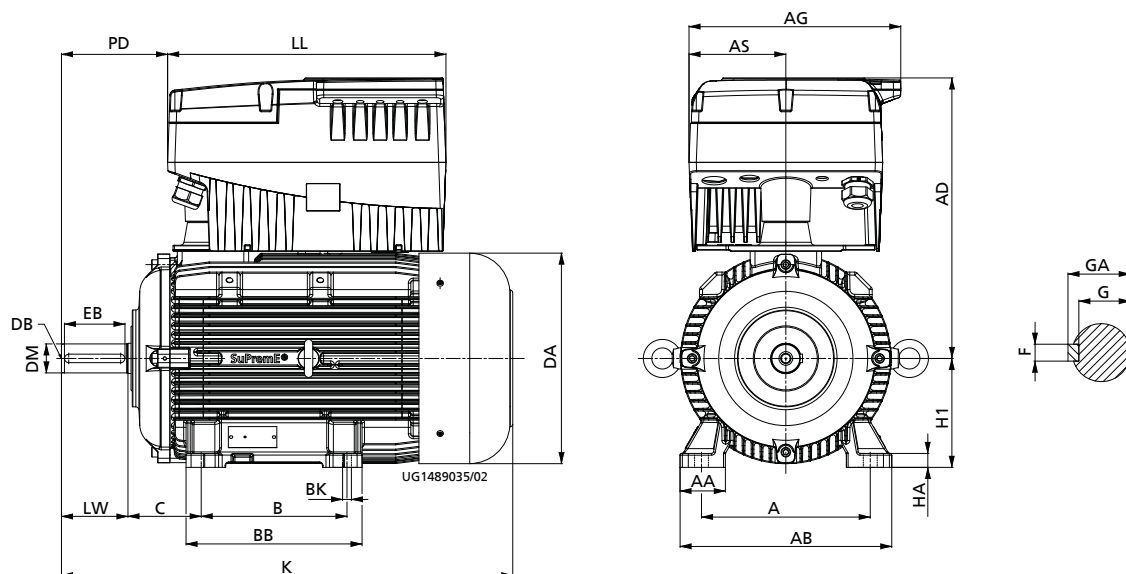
Исполнение со стандартной крышкой подшипника (B3,...)
